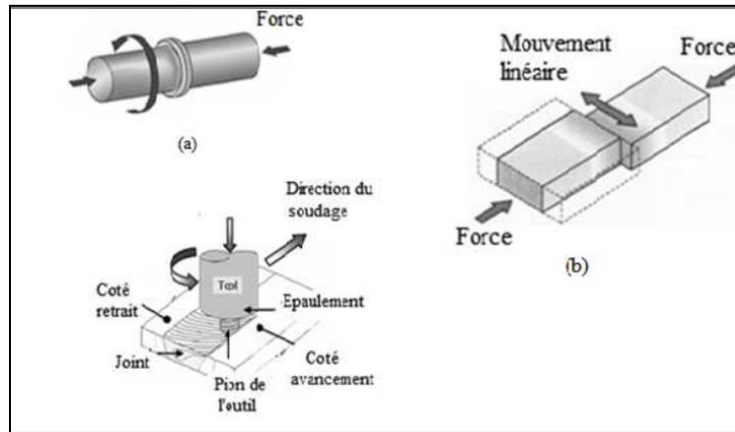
Principaux procédés de soudage par friction, a – Friction rotative, b – Friction linéaire, c – Friction malaxage (FSW)
